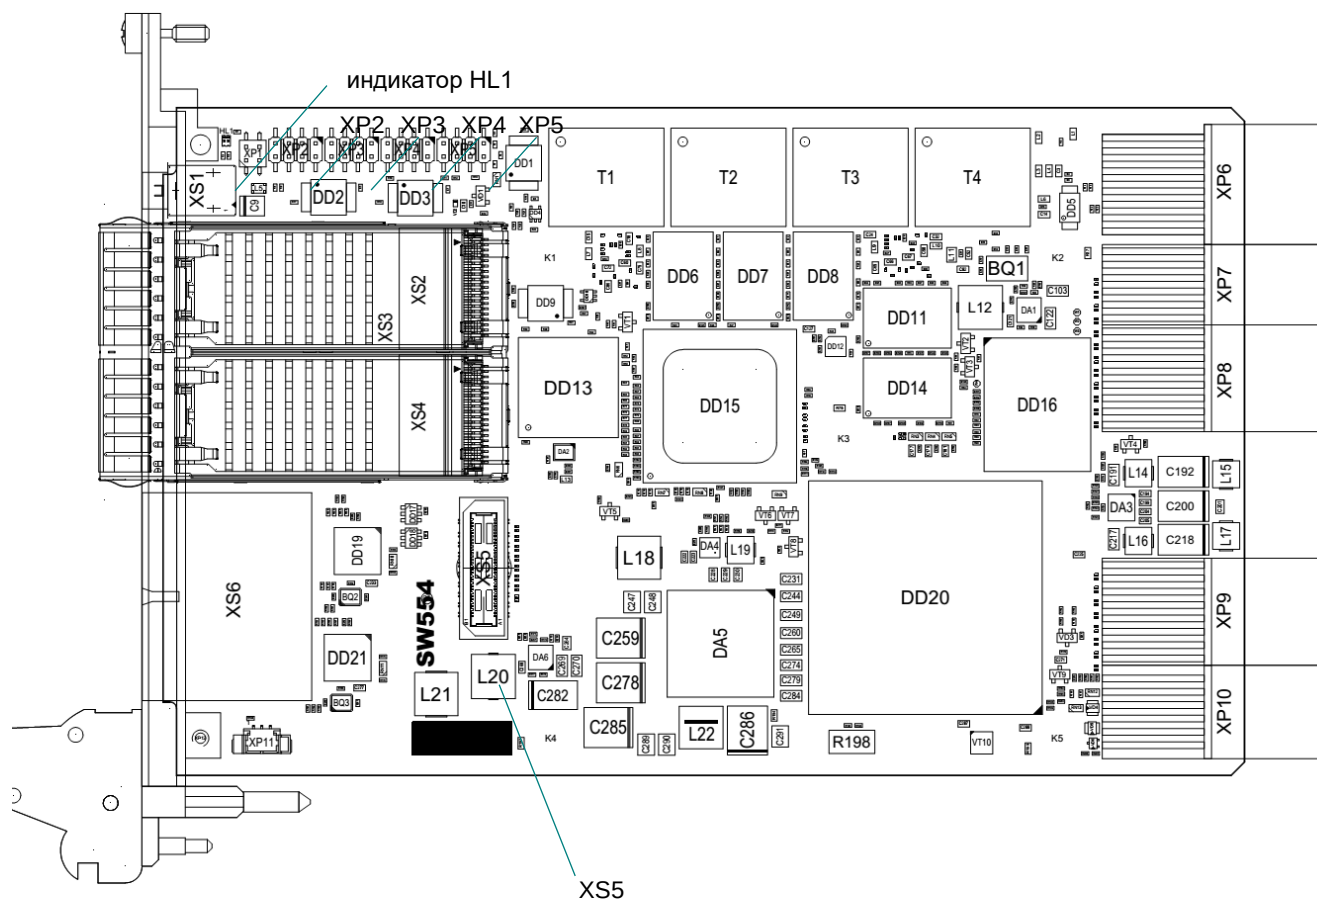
2 - Расположение основных компонентов изделия на плате (вид сверху)
